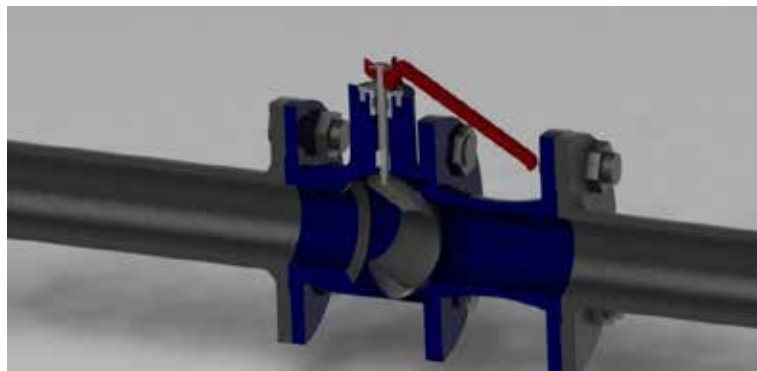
Sección de la Geometría CAD de la Válvula de Bola.
